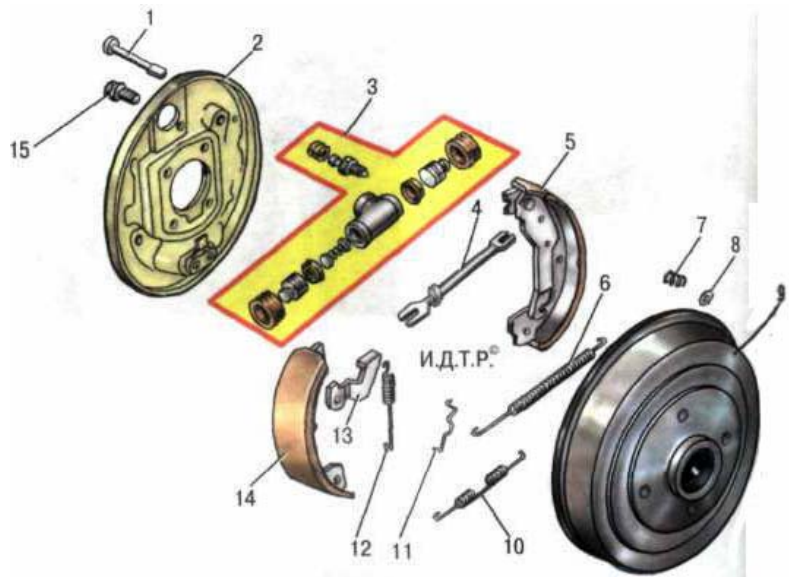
Детали заднего тормозного механизма: 1 - опорная стойка; 2 - щит тормоза; 3 - рабочий цилиндр; 4 - распорная планка с регулятором зазоров; 5 - задняя тормозная колодка; 6 - верхняя стяжная пружина; 7 - пружина опорной стойки; 8 - чашка опорной стойки; 9 - тормозной барабан; 10 - нижняя стяжная пружина; 11 - серьга регулятора зазоров; 12 - пружина регулятора зазоров; 13 - рычаг регулятора зазоров; 14 - передняя тормозная колодка; 15 - болт крепления рабочего цилиндра
